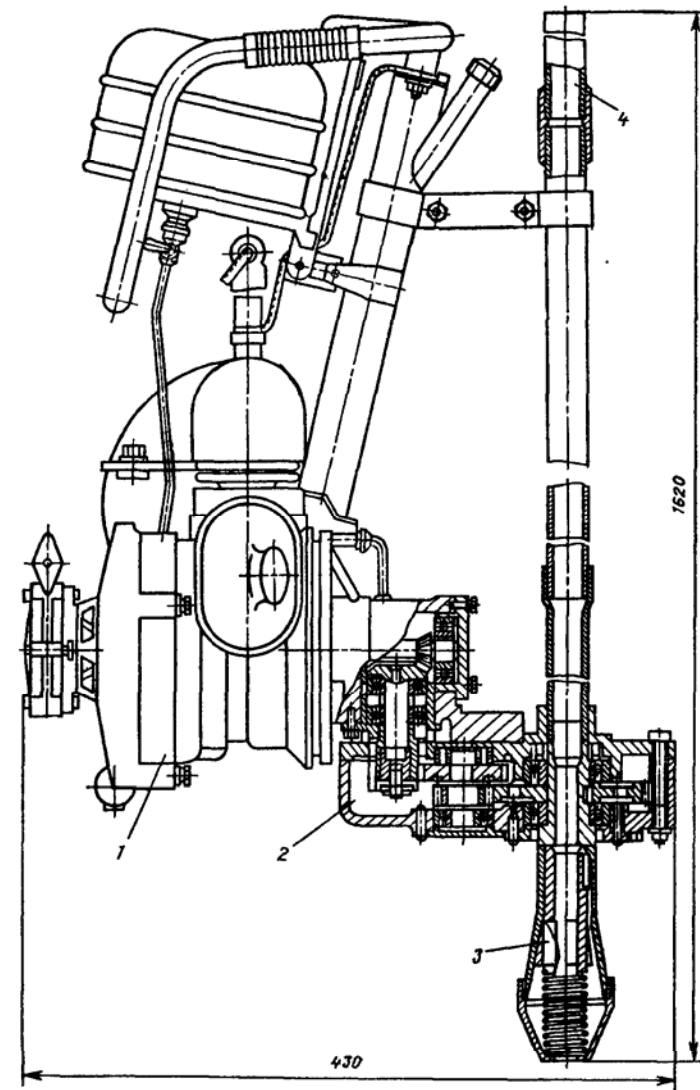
Приспособление ПЗД для ввертывания электродов заземления:
